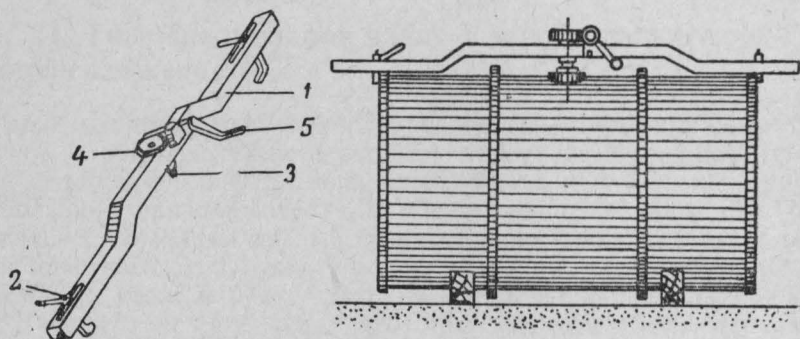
Приспособление для открывания бочек с ЛВЖ
